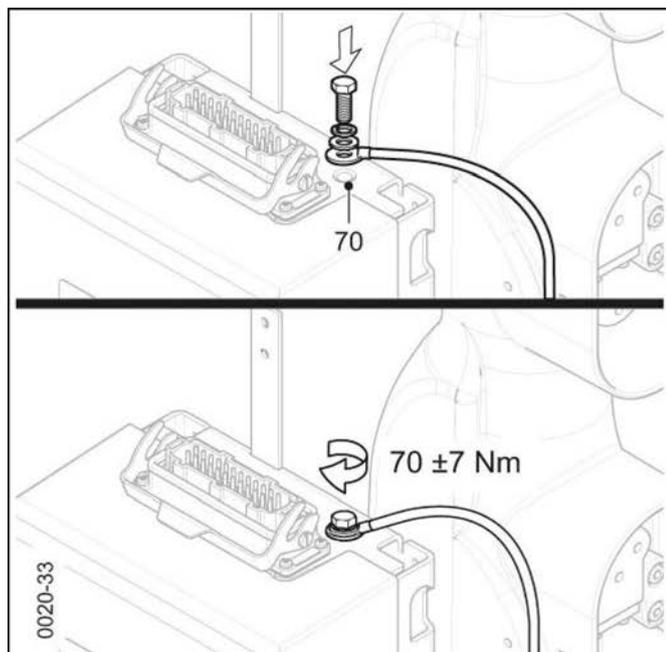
Подсоединение заземляющего провода к корпусу привода
